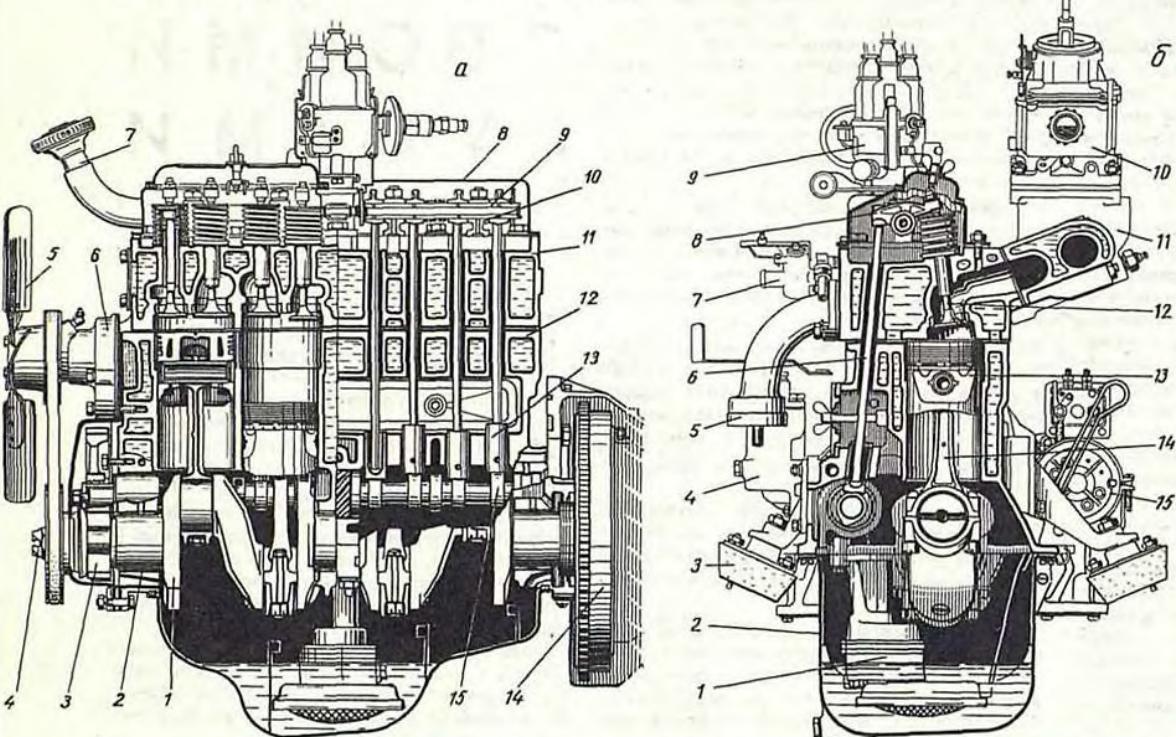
Двигатель «МосквиЧа-408». А — продольный разрез; 1 — щека коленчатого вала; 2 — коренная шейка; 3 — шестерня коленчатого вала; 4 — храповик; 5 — вентилятор; 6 — водяной насос; 7 — маслоналивная горловина; 8 — крышка головки блока цилиндров; 9 — валик коромысел; 10 — стойка коромысел; 11 — головка блока; 12 — блок цилиндров; 13 — толкатель; 14 — маховик; 15 — кулачок. Б — поперечный разрез: 1 — масляный насос; 2 — масляный картер; 3 — подушка подвески двигателя; 4 — фильтр грубой очистки масла; 5 — выпускной трубопровод; 6 — штанга толкателя; 7 — кран отопителя кузова; 8 — коромысло; 9 — распределитель зажигания; 10 — карбюратор; 11 — выпускной трубопровод; 12 — выпускной клапан; 13 — поршень; 14 — шатун; 15 — стартер.
